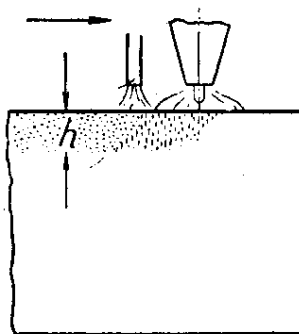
Схема газопламенной поверхностной закалки (h – глубина закаленного слоя)
